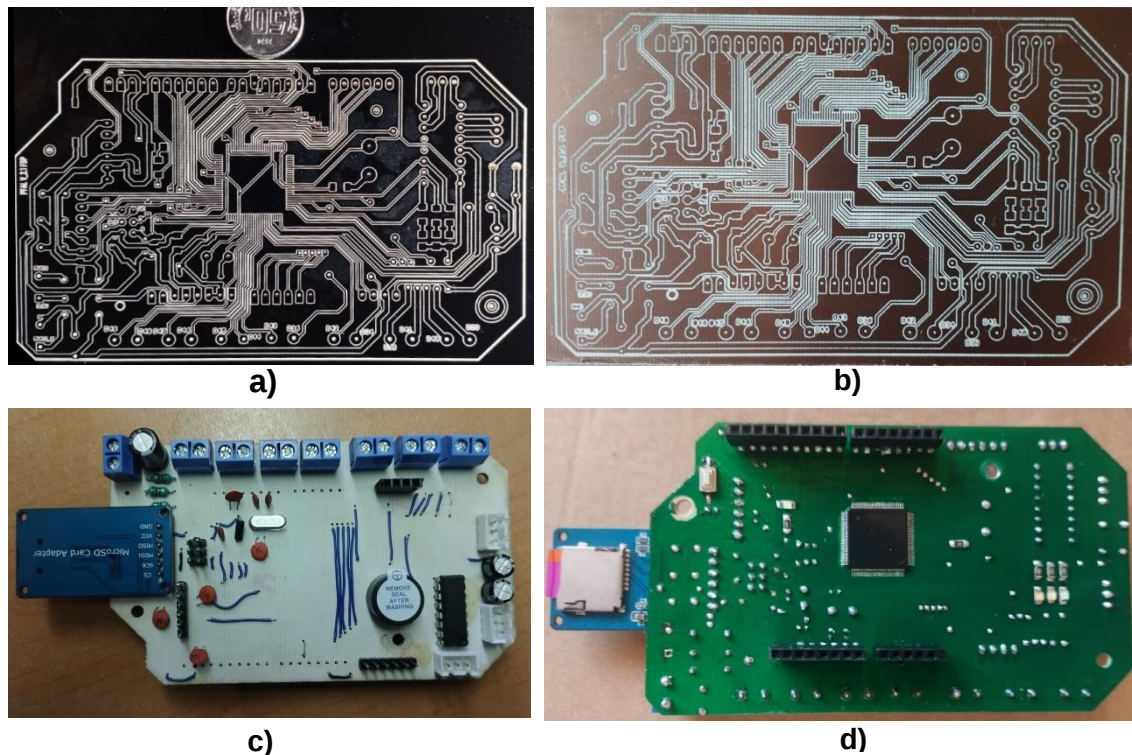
PCB fabricada de manera manual a) Primera etapa: capa de pintura con el diseño de la PCB, b) Segunda etapa: proceso del baño en cloruro férrico y limpieza, c) PCB terminada vista posterior, d) PCB terminada vista frontal
